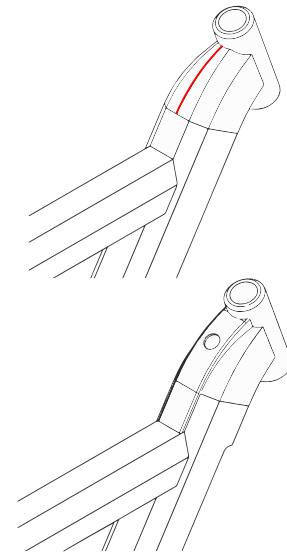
Zona de união entre o tubo interior e o cilindro da direção.
